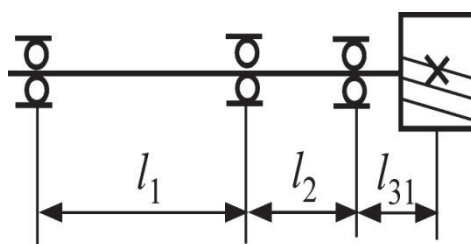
Расчетная схема трехопорного вала с шестерней, расположенной консольно
